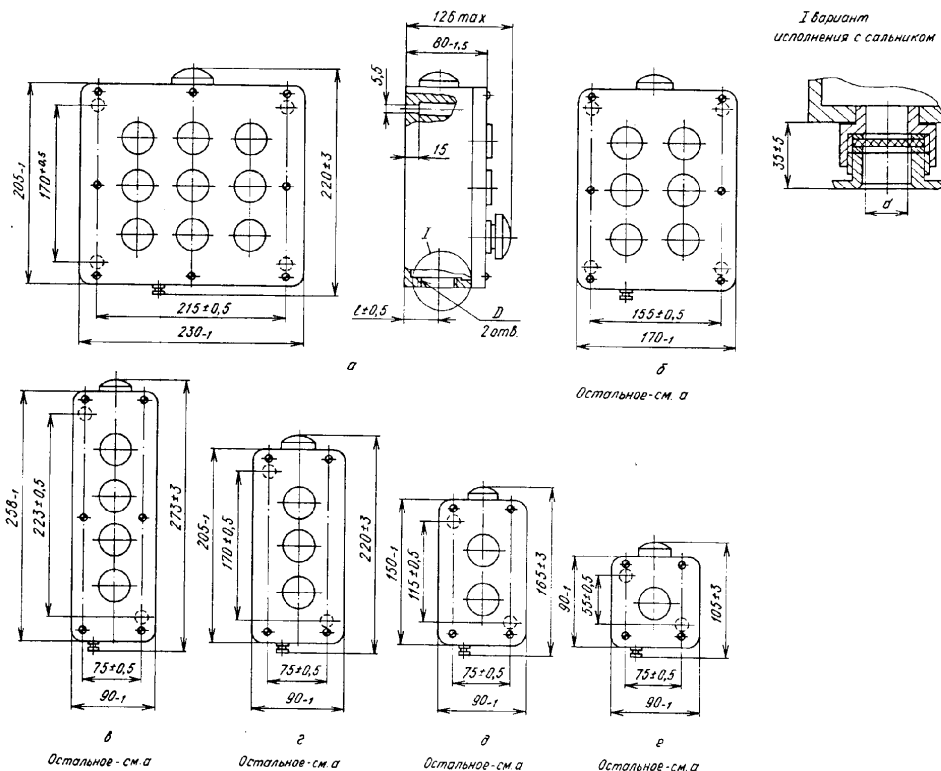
Габаритные, установочные, присоединительные размеры и масса постов, выполненных по способу установки для пристройки к плоской поверхности
